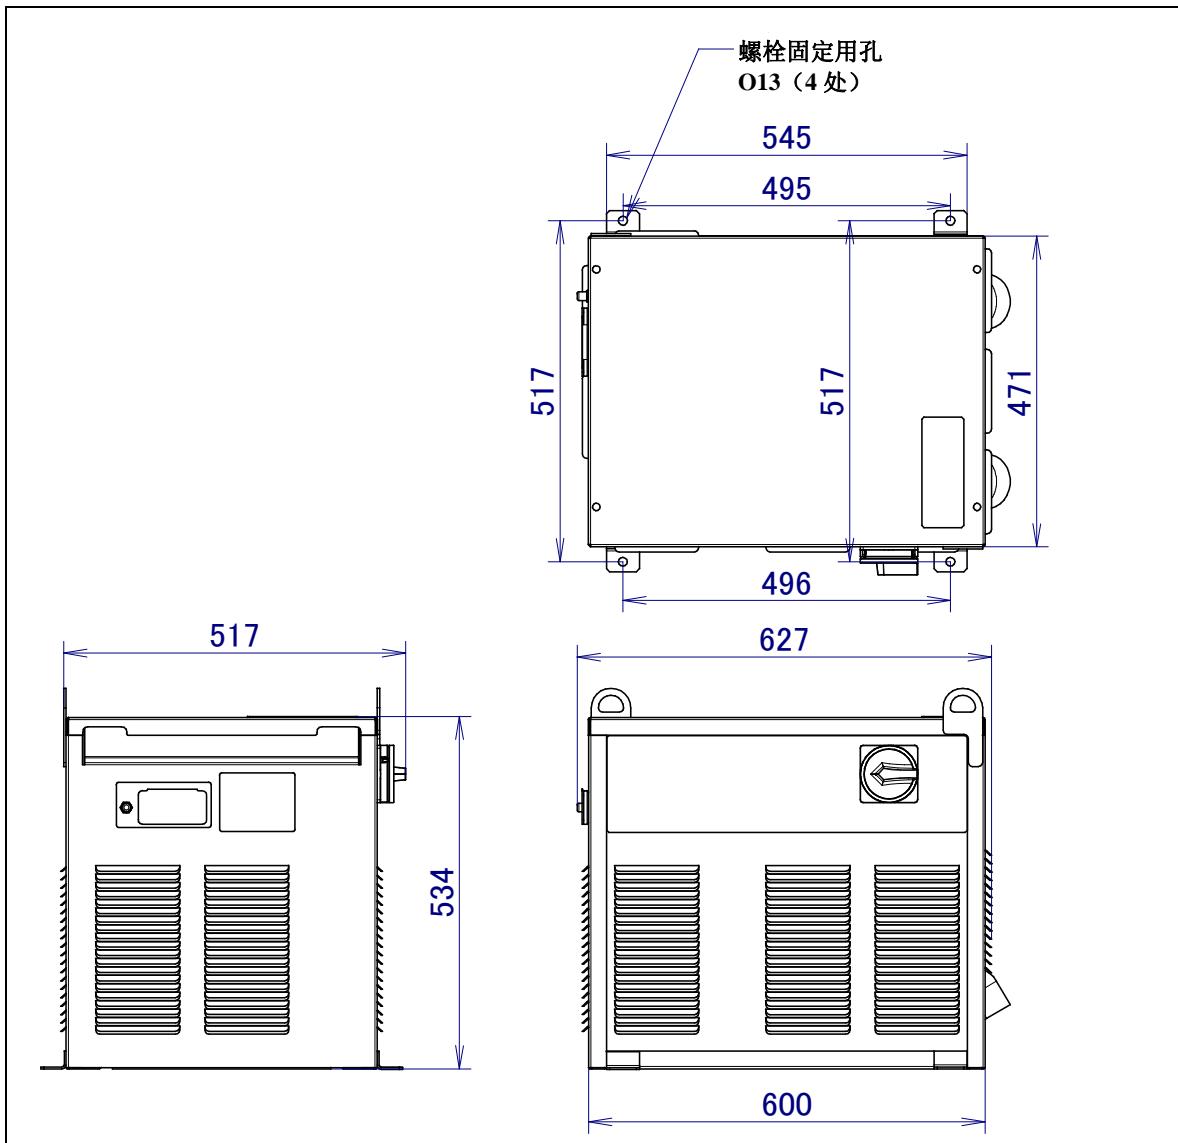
(a) ROBOWELD iC/H 用焊接电源 (Power Wave i400)
